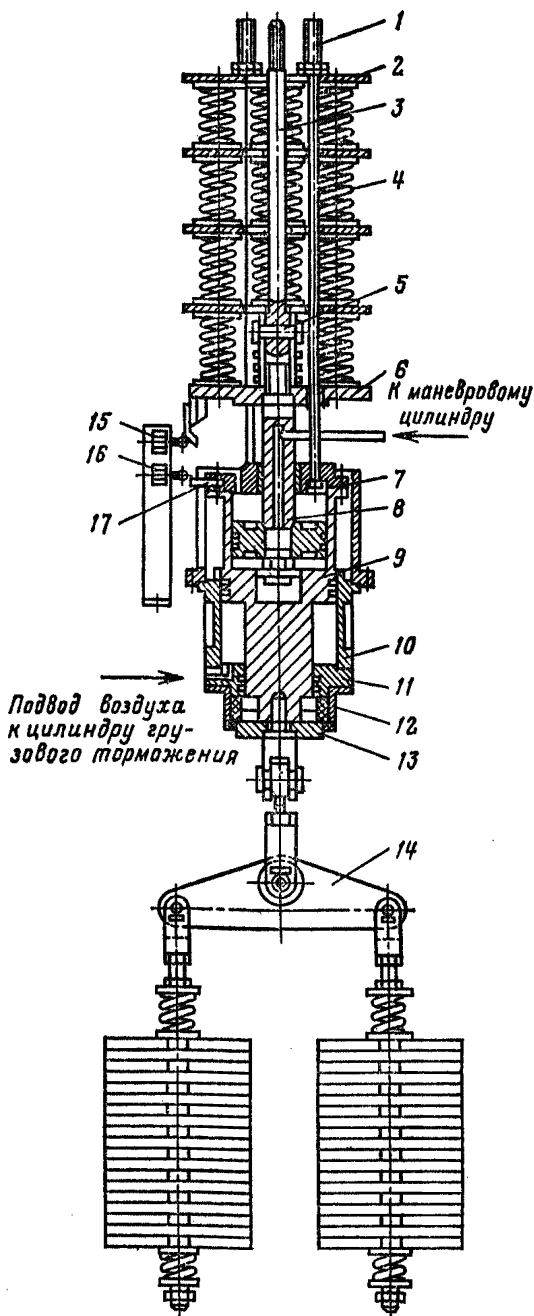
Пружинно-грузовой пневматический привод тормоза:
